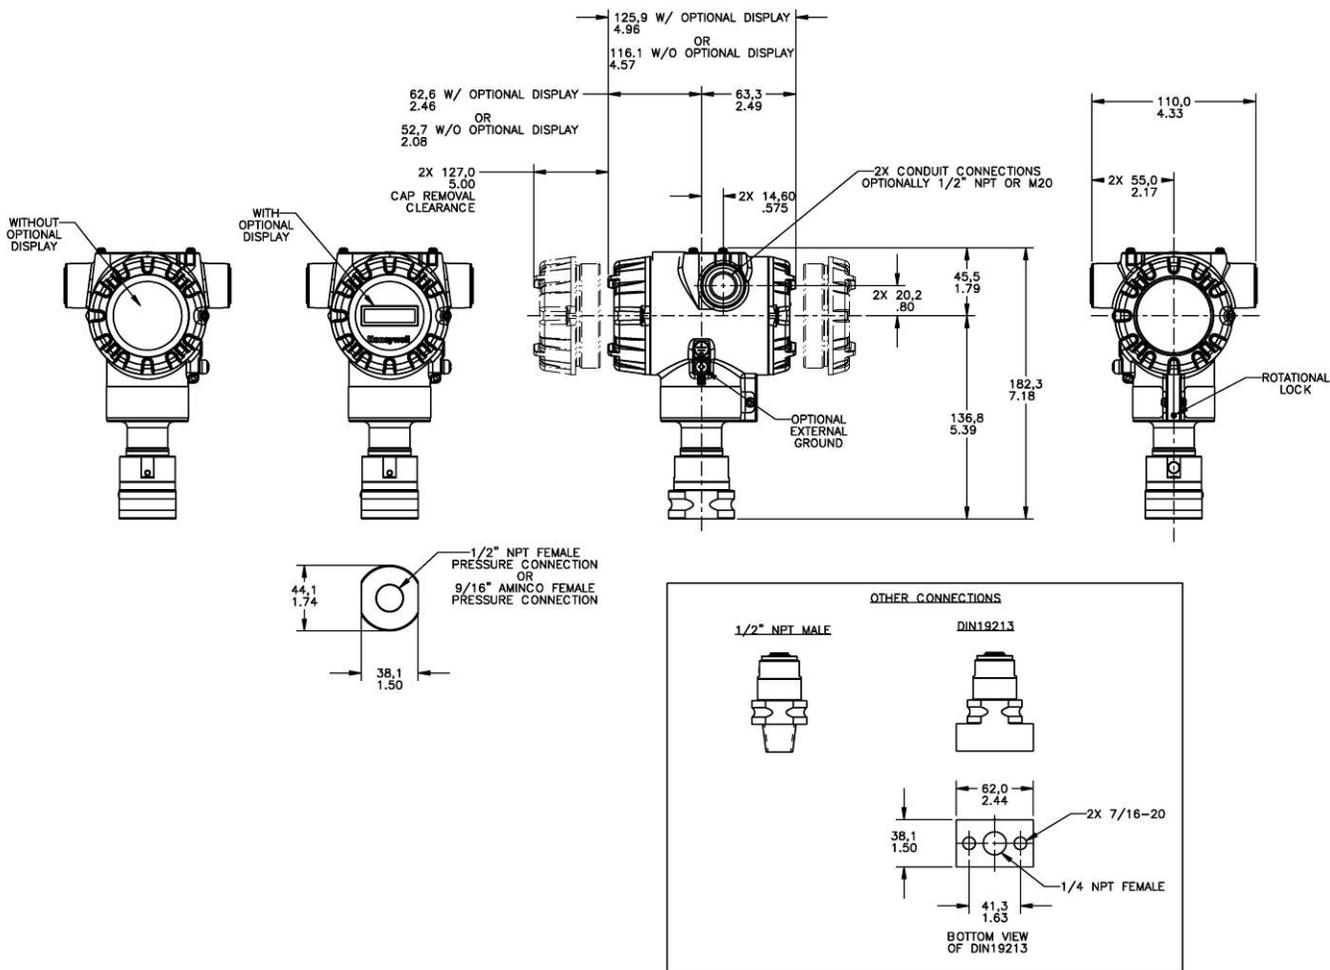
Dimensiuni tipice de montaj pentru STG84L, STG87L, STG88L si STG89L ca referinta
